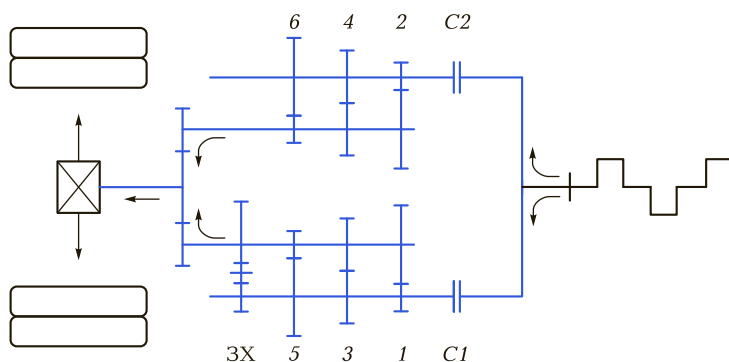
Схема коробки передач с двумя сцеплениями:
